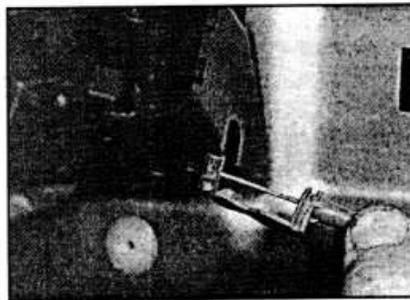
Отсоединение тяги открытия замка от внутренней ручки открытия двери.
